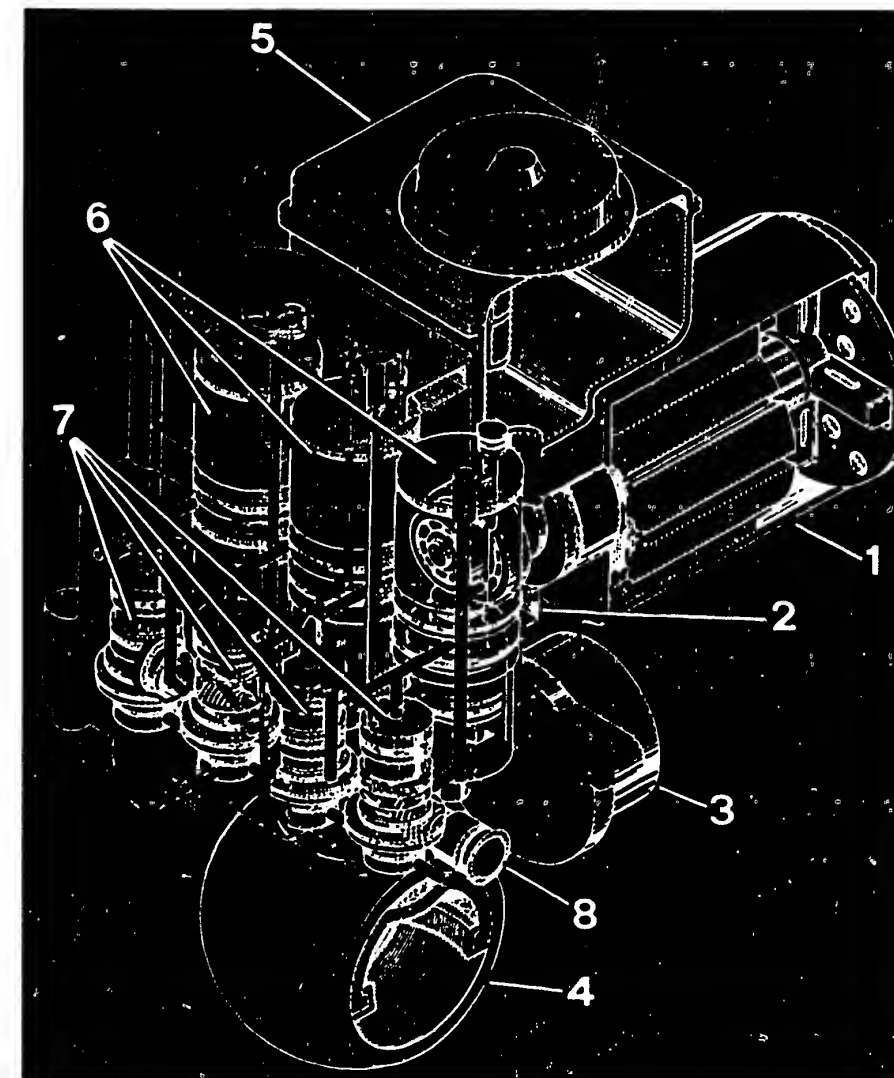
Hydraulik-Einheit im Schnitt: 1 Elektromotor – 2 Hydraulikpumpe – 3 Druckschalter – 4 Druckspeicher – 5 Flüssigkeitsreservoir – 6 Magnetventile – 7 Steuerkolben – 8 Reduzierventile.
